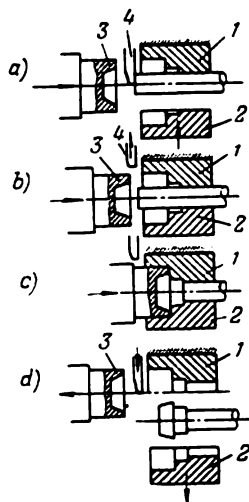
Schéma du fonctionnement d'une machine à forger horizontale
